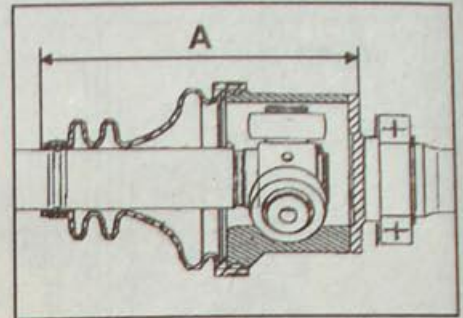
Измерение расстояния между торцом корпуса шарнира и концом защитного чехла:
